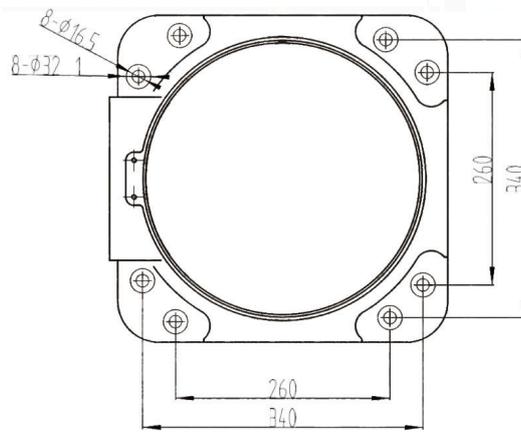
Габаритные и присоединительные размеры фланца робота-манипулятора
